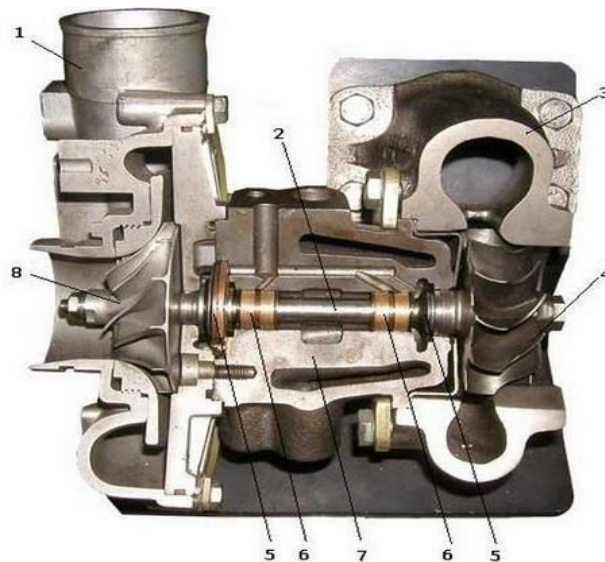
Конструкция турбоагнетателя: 1 — корпус компрессора; 2 — вал ротора; 3 — корпус турбины; 4 — турбинное колесо; 5 — уплотнительные кольца; 6 — подшипники скольжения; 7 — корпус подшипников; 8 — компрессорное колесо.
